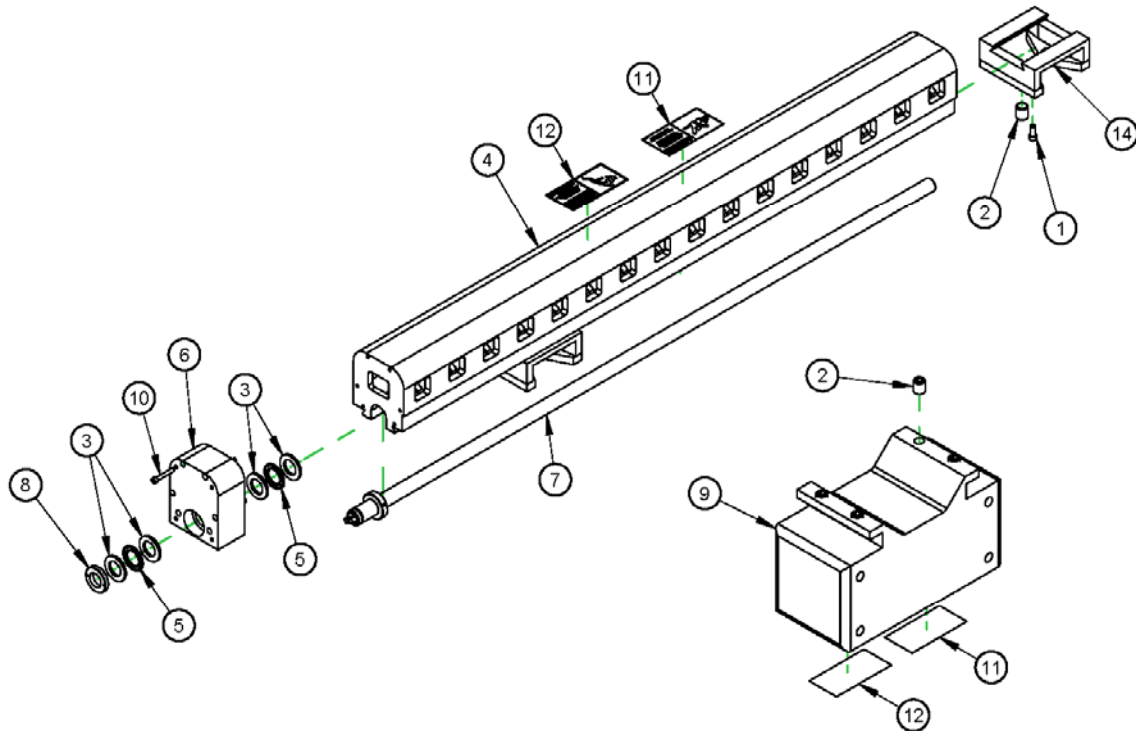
Основной корпус PL4000 в сборе Н/Д 13142
